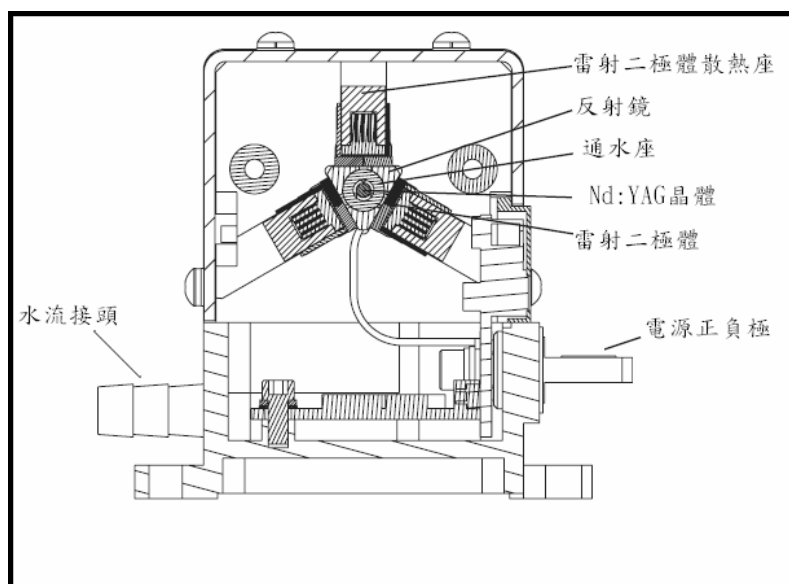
Cutting Edge Optonics RB 系列 DPSS Nd : YAG Rod Laser module
